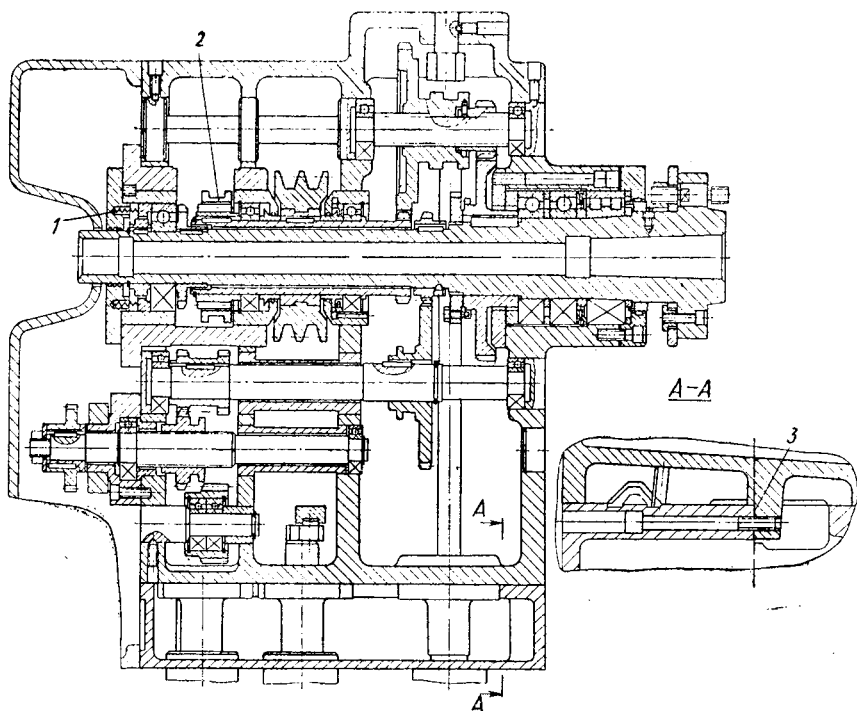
Развертка шпиндельной бабки станка 16Б04П
